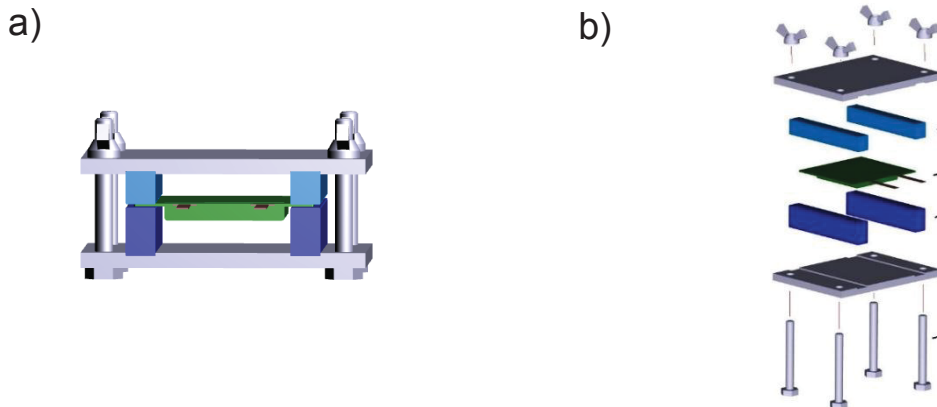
Support pour cellules 53437 a) vue de face et b) vue éclatée.
